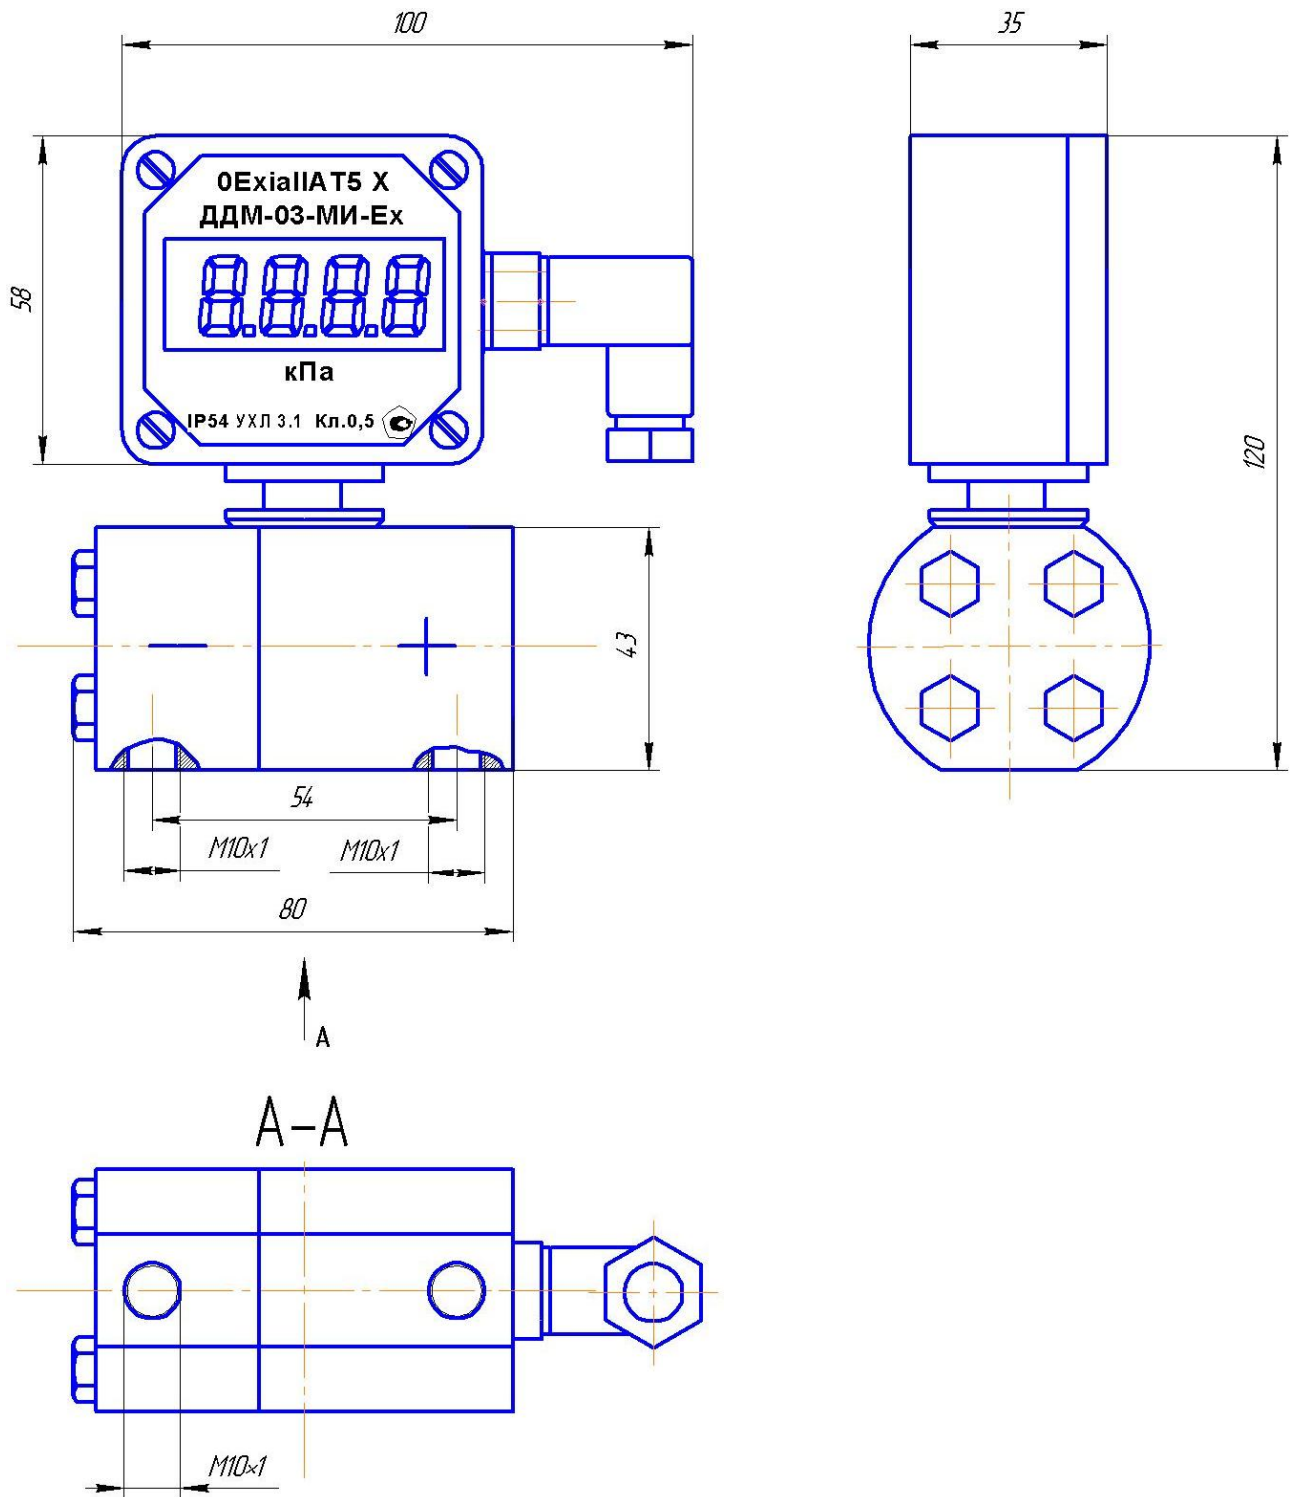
Габаритные и присоединительные размеры датчика ДДМ-03-ДД-МИ; ДДМ-03-ДД-МИ-Ех.
